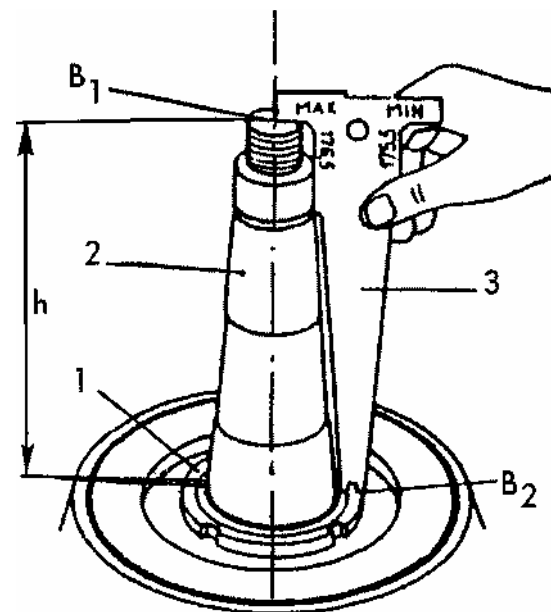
Проверка положения напорного диска по высоте h относительно верхнего конца вала. 1-затяжная гайка; 2-вал; 3-шаблон; b_1 -верхний зазор; b_2 - нижний зазор.
